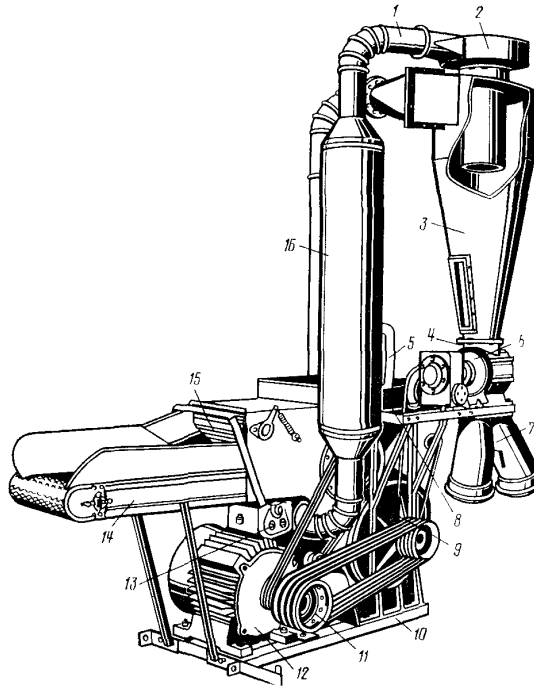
Универсальная дробилка кормов КДУ-2: 1 – обратный трубопровод; 2 – улитка циклона; 3 – циклон; 4 – редуктор шлюзового затвора; 5 – рамка амперметра-индикатора; 6 – шлюзовой затвор; 7 – раструб циклона; 8 – приемный бункер; 9 – дробильная камера; 10 – рама; 11 – шкив с фрикционной муфтой; 12 – электродвигатель; 13 – редуктор; 14, 15 – прессующий и подающий транспортеры; 16 – фильтр
